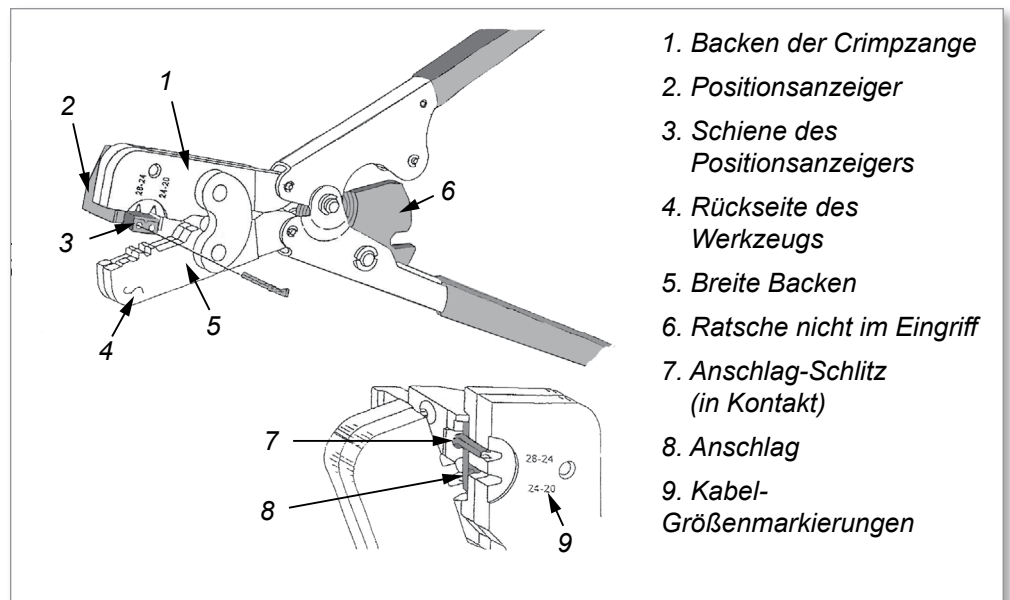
QDISC – CRIMP-Werkzeug
